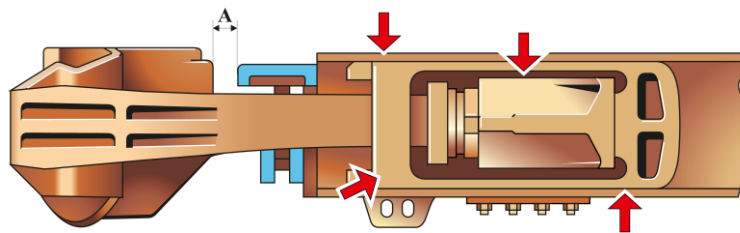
Расстояние от упора корпуса автосцепки до розетки более установленных норм
